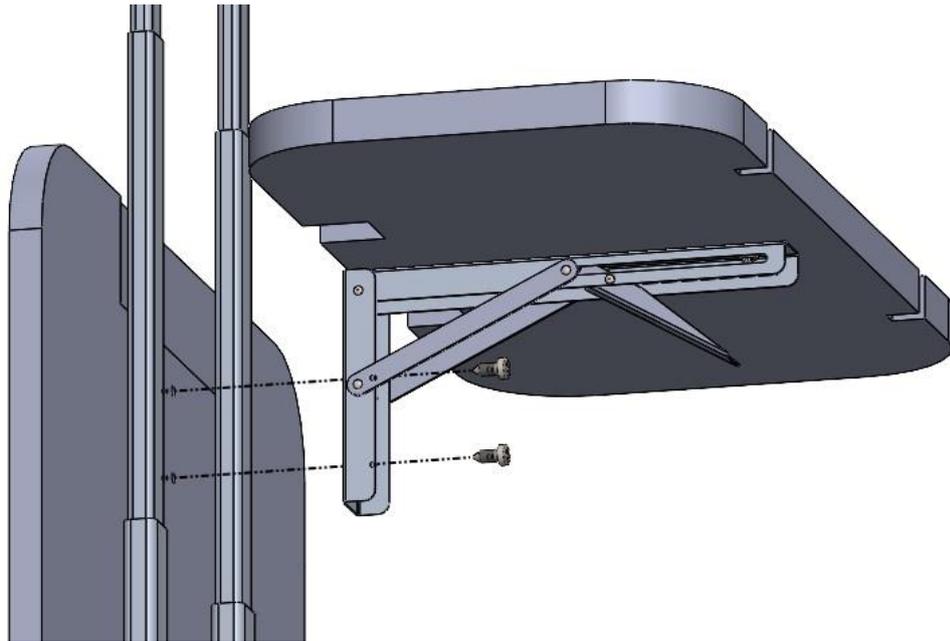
Ensamblaje subconjuntos 1 y 6 (3)
